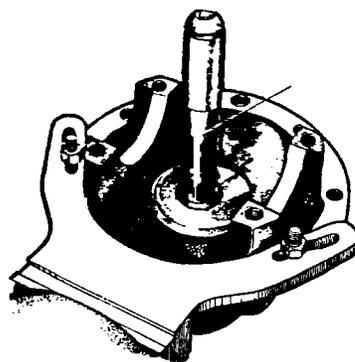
Установка с помощью оправки наружного кольца заднего подшипника ведущей шестерни: 1 - оправка А.70171
